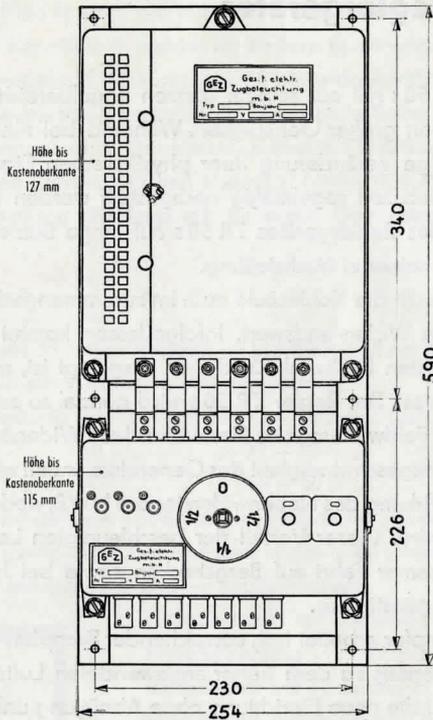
Maßbild für Reglergerät ZR 50s mit Schaltkasten ZS auf Montagerahmen
